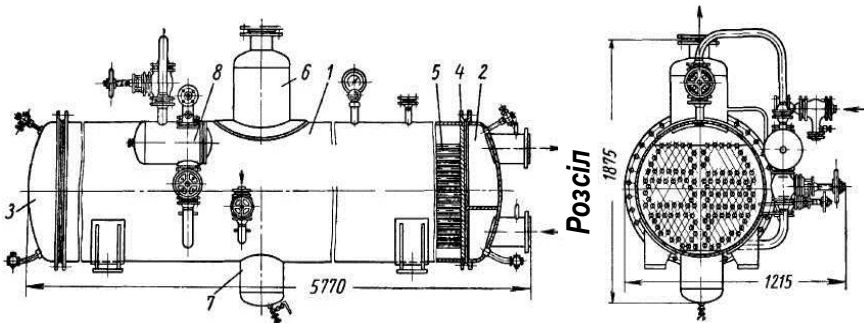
Аміачний кожухотрубний випарник: 1 – корпус; 2, 3 – кришки; 4 – трубні ґрати; 5 – труби; 6 – сухопарник; 7 – відстійник, 8 – поплавковий регулюючий вентиль
